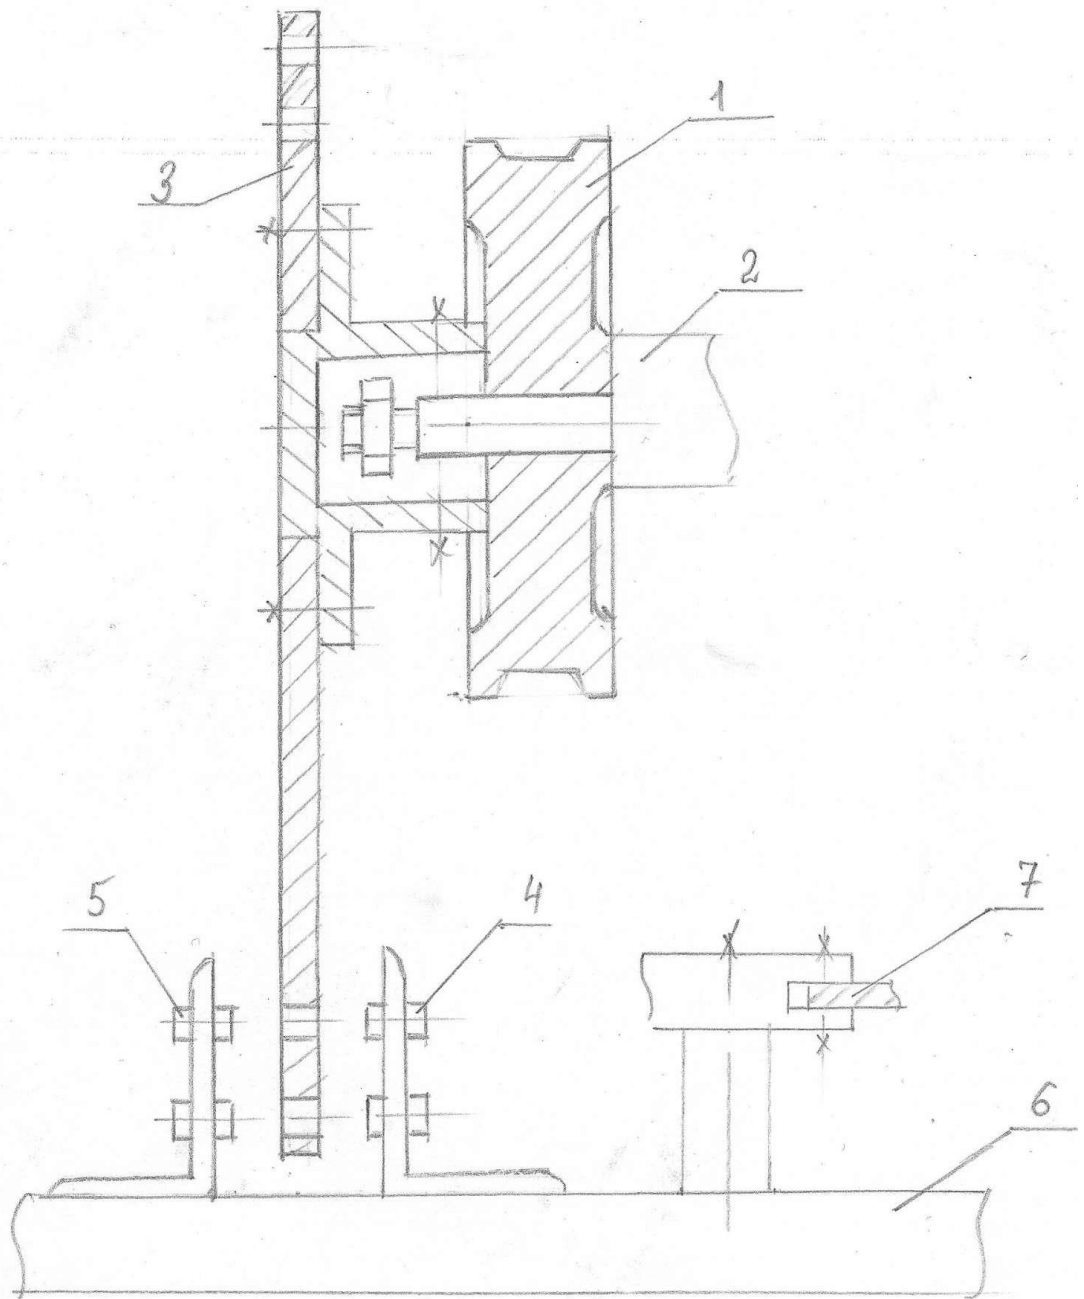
Схема пристрою для вимірювання кута повороту головного валу машини
